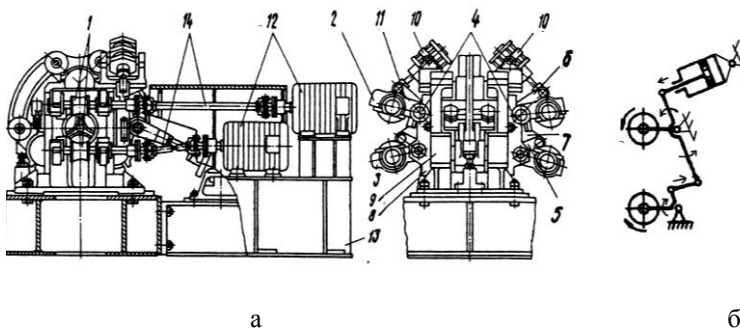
Пристрій для видалення гільз зі стану : загальний вигляд (а) та кінематична схема механізму хитання (б)
